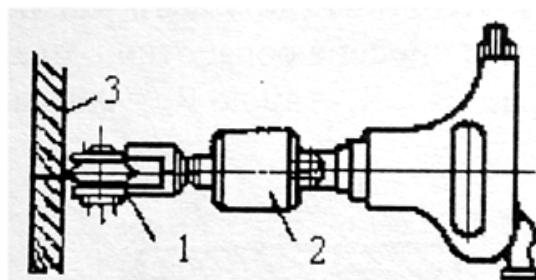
Схема обработки чеканкой: 1 – ролик; 2 – отбойный молоток; 3 – обрабатываемая деталь
